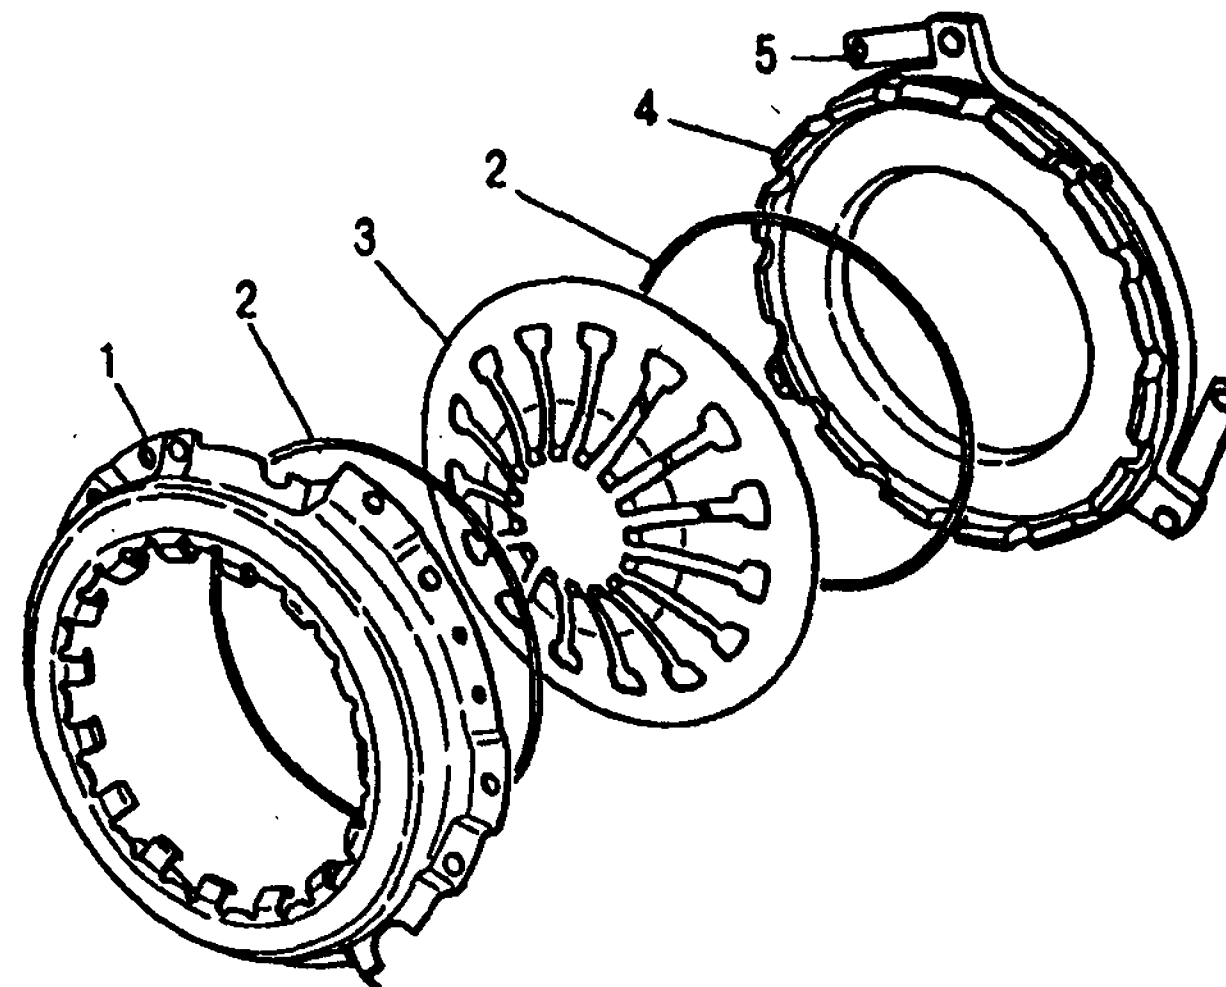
Детали ведущего диска: 1 - кожух; 2 - опорное кольцо; 3 - нажимная диафрагменная пружина; 4 - нажимной диск; 5 - соединительная пластина
